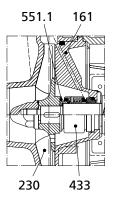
Сборочный чертеж, типоразмер двигателя IEC 200
